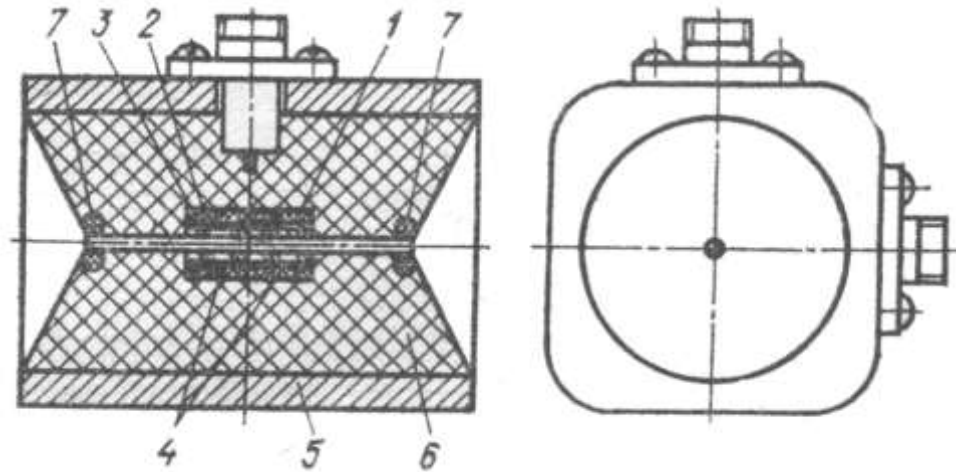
Конструкція прохідного диференціального вихорострумів перетворювача для контролю дроту: 1 – каркас; 2 – збуджувальна навитка; 3 – втулка; 4 – вимірювальні навитки; 5 – латунний корпус; 6 – компаунд; 7 – керамічна втулка
